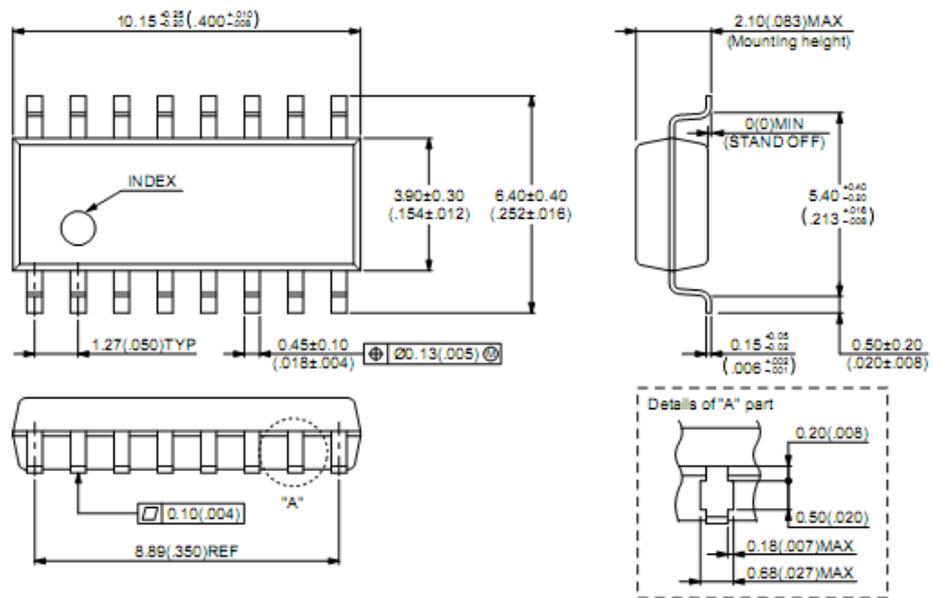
Габаритные и установочные размеры корпусов типа FPT-16P-M04
